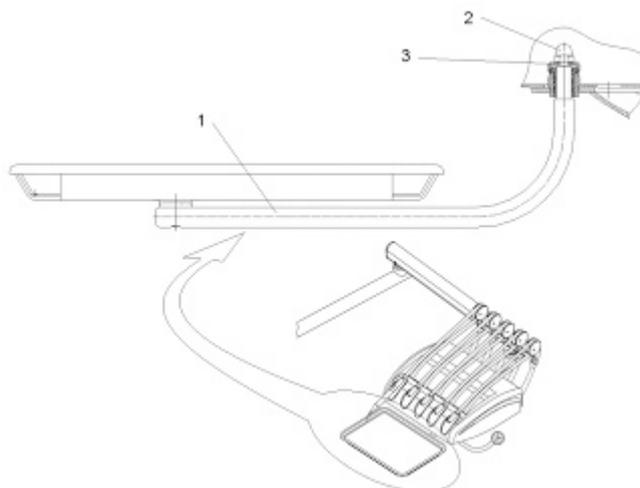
Установка поворотного столика блока с верхней подачей
